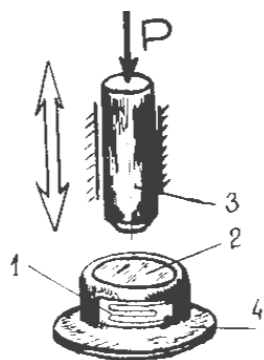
Схема вибивання скла з кришки ФД:
